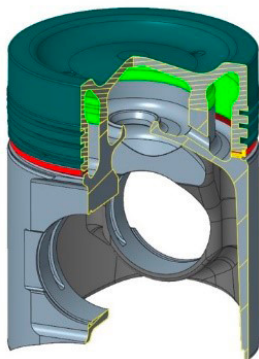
Konstruierter thermomechanisch reibgeschweißter Kolben für den FM29/24
